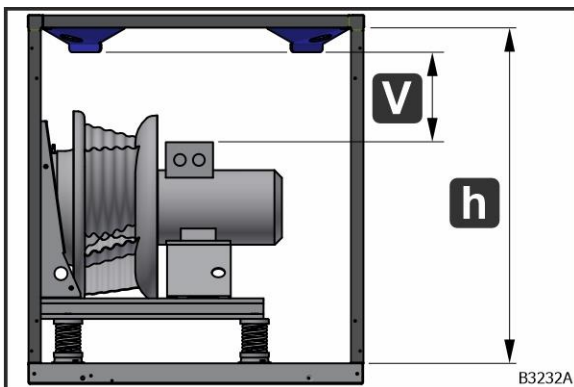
Samenstelling van de motoruitbouwvoorziening
